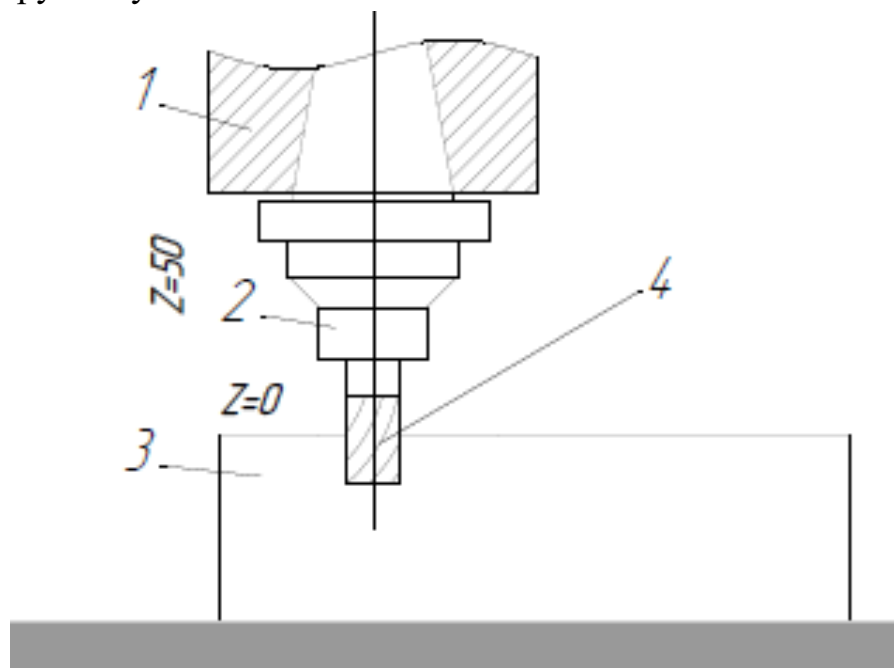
Переміщення інструментального блоку 80мм в координату Z50 без компенсації довжини призведе до зіткнення інструменту із заготовкою: 1 – шпиндель верстата; 2 – затискний патрон; 3 – заготовка; 4 – різальний інструмент.
